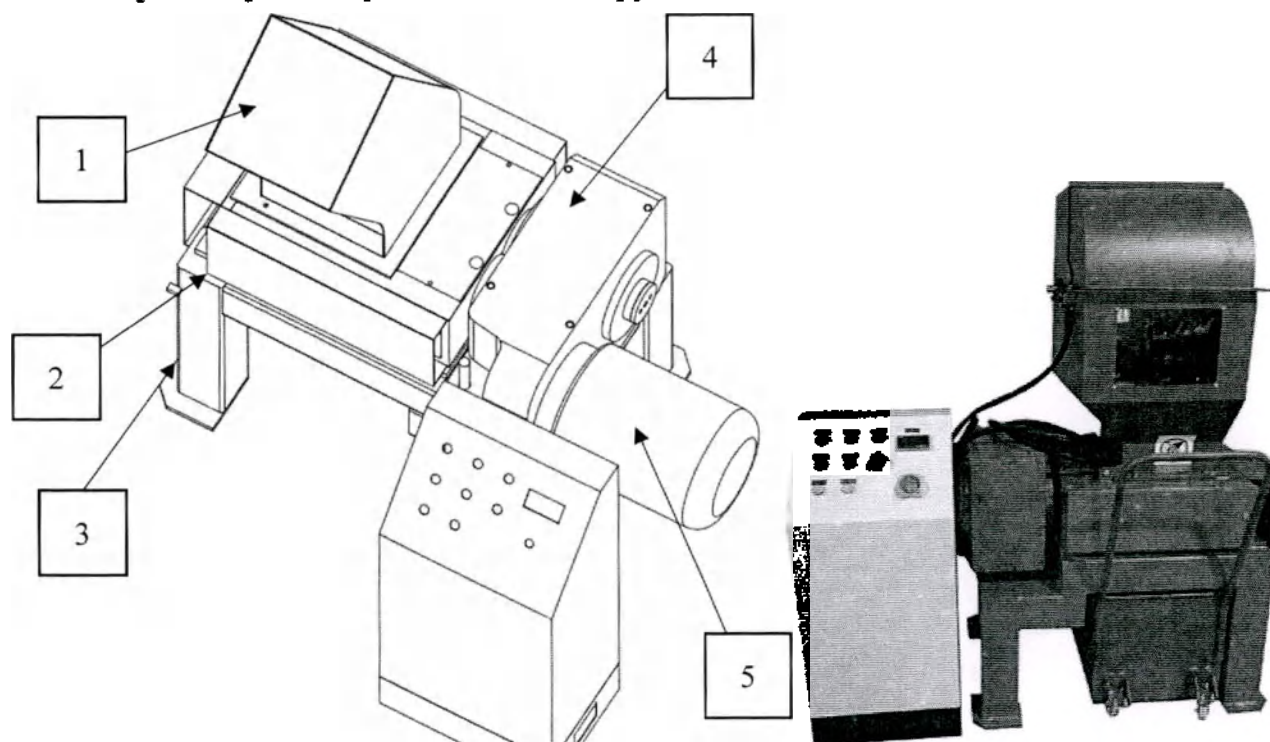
Структурная схема и внешний вид модуля 2 конструктивно-функциональных элементов, где: 1 – Воронка; 2 – Камера для резки; 3 – Корпус; 4 – Редуктор; 5 – Электродвигатель;
